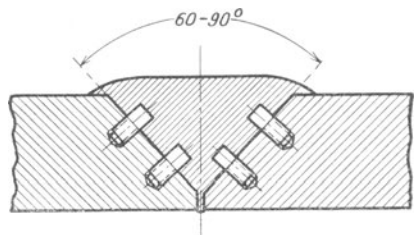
Elektrisches Kaltschweißen (Einsetzen von Gewindestiften).
